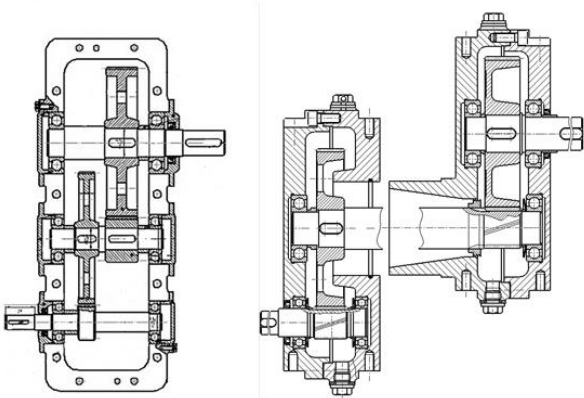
Разделение общего корпуса редуктора на два отдельных с общим промежуточным валом
